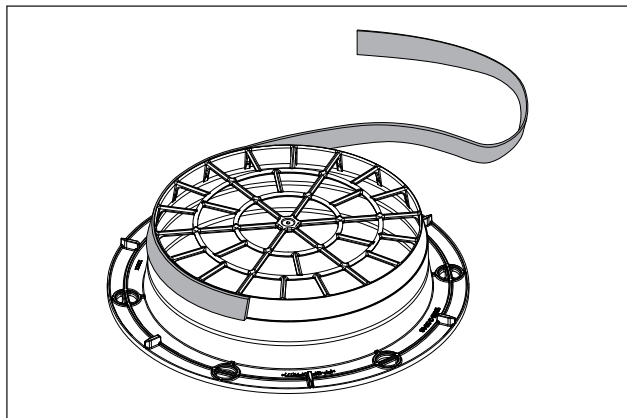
Posição da cinta vedante para montagem com tubo redondo
